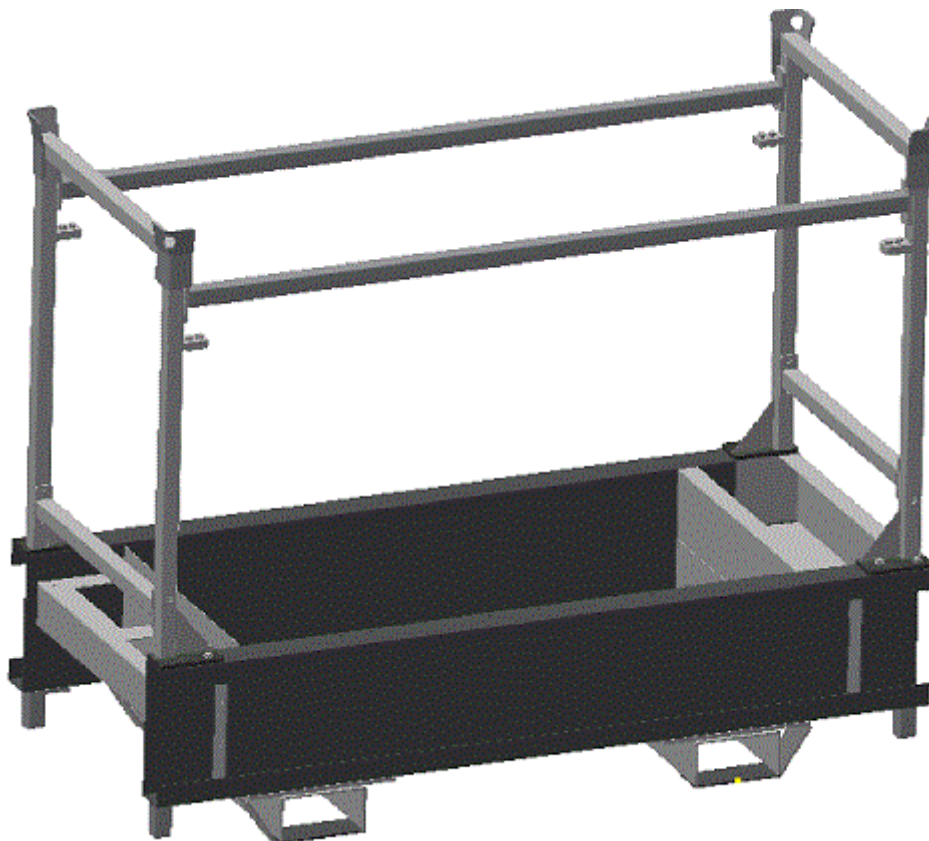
První konstrukční varianta nosné konstrukce
